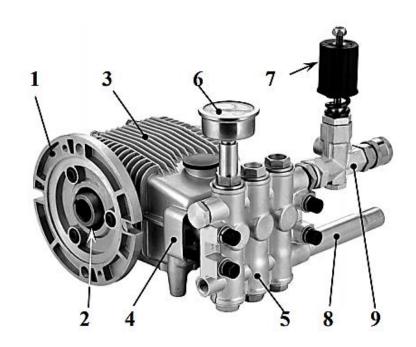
Поршневой блок жидкостного трехцилиндрового насоса: 1 — фланец для монтажа электродвигателя; 2 — приводной вал; 3 — механизм привода; 4 — блок цилиндров; 5 — клапанный блок; 6 — манометр; 7 — предохранительный клапан; 8 — всасывающий патрубок; 9 — нагнетательный патрубок
